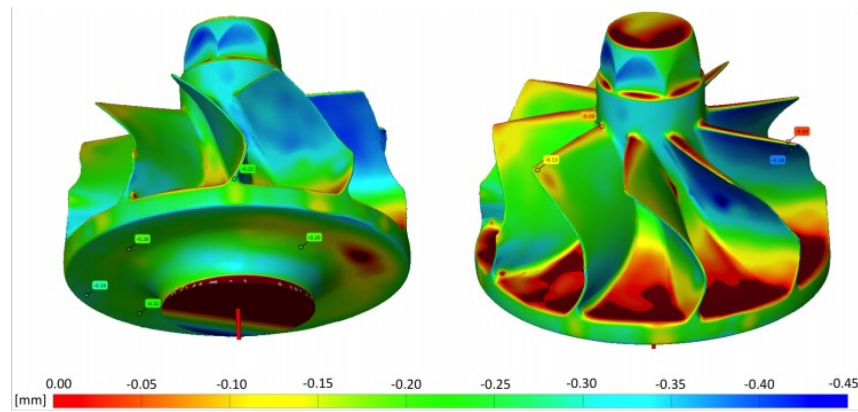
Controlo dimensional de turbina *near-net shape* maquinada quimicamente durante 40 minutos [42]
